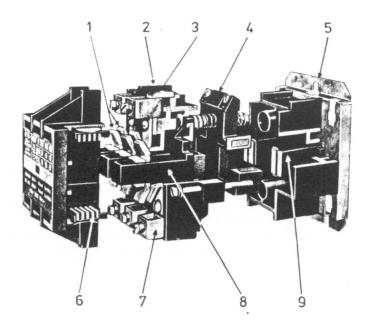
Estructura del contactor AGUT tipo CK: 1.Contactos fijos y móviles de diseño especial, con plaquitas de contacto de plata-óxido de cadmio, soldadas, 2.soporte de contactos fijos moldeado con material aislante, altamente resistente a las líneas de fuga, 3.Bobina completamente encapsulado para su completa protección mecánica y atmosférica, 4.Bornes para embornar pletinas y terminales, 5.Soporte de base metálico con alejamiento en cada esquina para bloque de dos contactos auxiliares, 6.Extintores de arco De-ión, alojados en tapa frontal moldeada con material aislante altamente resistente al arco, 7.Bornes tipos mordaza, de gran capacidad y fácilmente accesibles, 8.Soporte portacontactos móviles y portamertillo moldeado con material aislante altamente resistente al arco, 9.Circuito magnético en forma de U y con entrehierro fijo.
